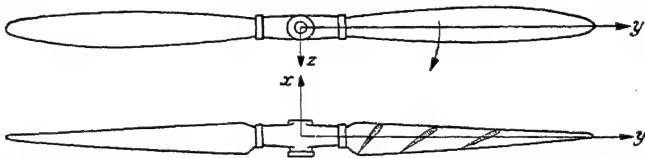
Einführung der Koordinaten x , y , z einer Schraube mit geradachsigen Flügeln. Die gezeichnete Schraube ist eine rechtsgängige Zugschraube.
